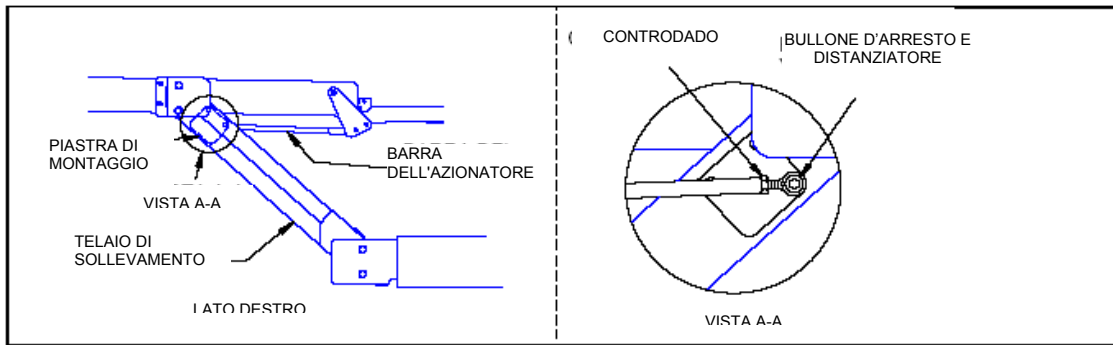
ESTRAZIONE DELLA BARRA DELL'AZIONATORE DALLA SPONDA DI COLLEGAMENTO
